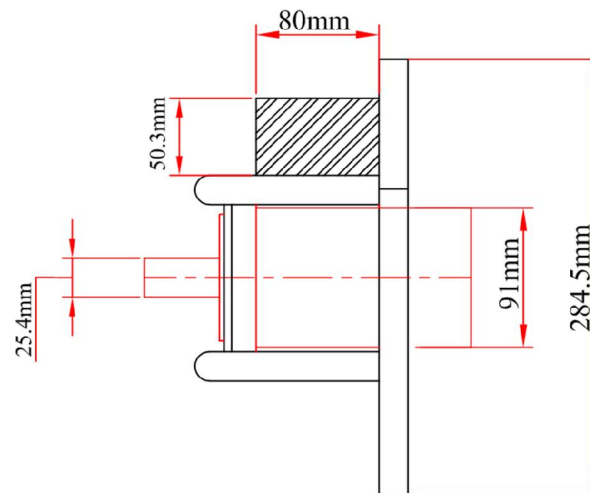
Detalhes das dimensões do motor hidráulico e bloco manifold
